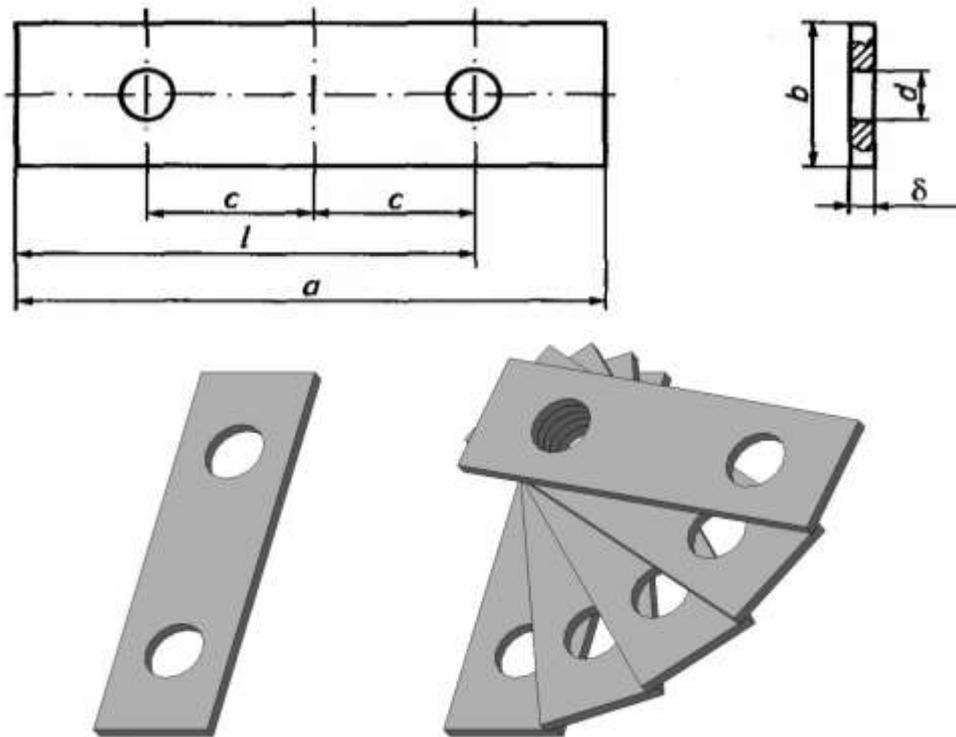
Прямоугольный молоток молотковой дробилки [29]
